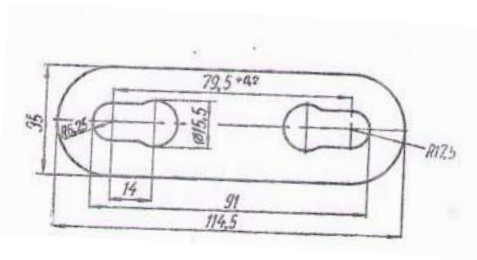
Планка транспортеру ТВК-80А (деталь ТВК-4124)
